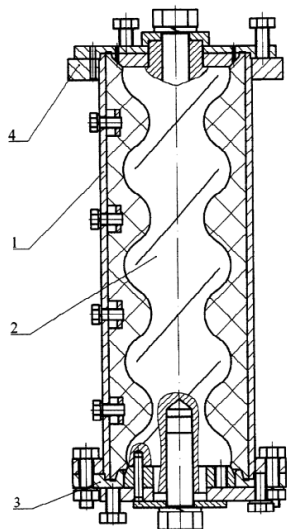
Общий вид литейной формы: 1 – корпус; 2 – литейный стержень; 3 – нижний фланец с выпорами; 4 – верхний фланец
